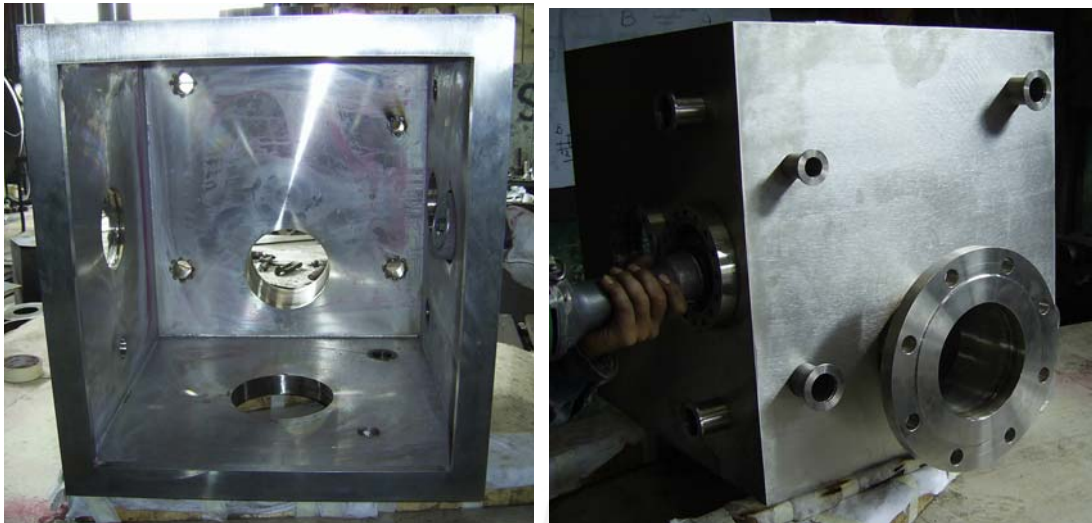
Izquierda: vista frontal luego del armado y soldadura de las caras que conforman la cámara. Derecha: cámara con las conexiones DN40, DN25 y la conexión embreada para la bomba de alto vacío.
